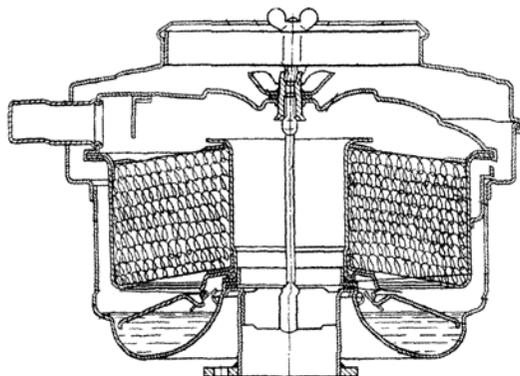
Воздушный фильтр двигателя ЗИЛ
